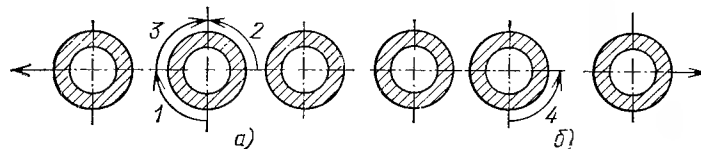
Порядок наложения валиков первого слоя шва вертикального стыка труб поверхностей нагрева при тесном расположении труб.
